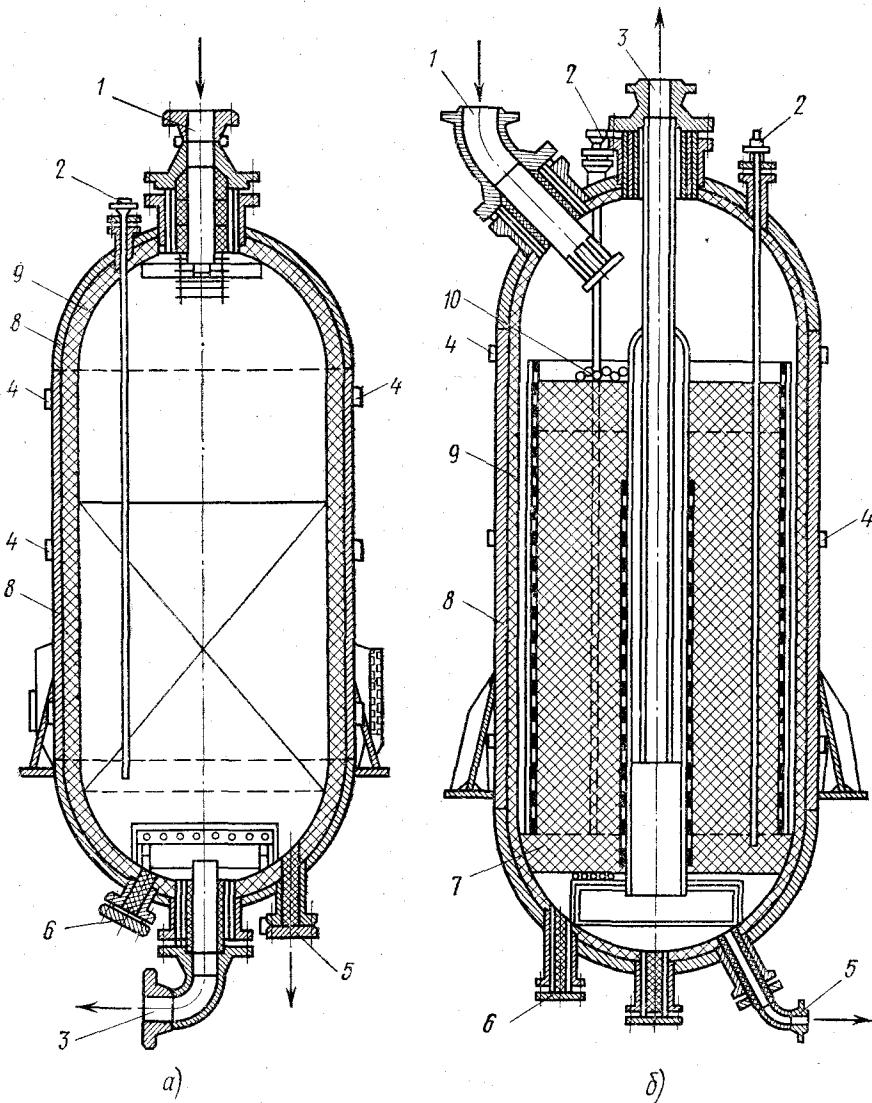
Реакторы установки Л-35-11/300 с аксиальным движением газо-сырьевой смеси:
